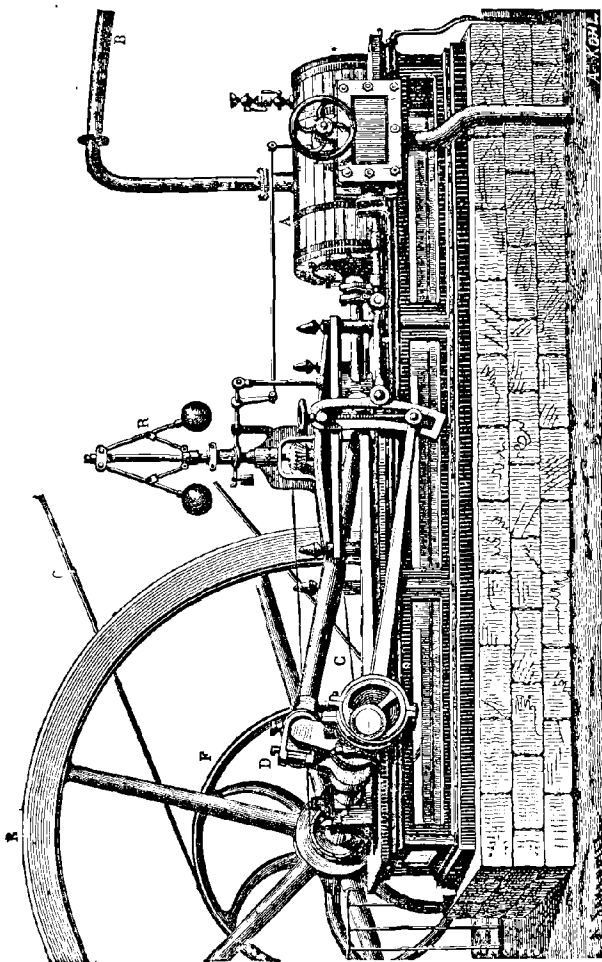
Machine sans condenseur, à cylindre horizontal.
